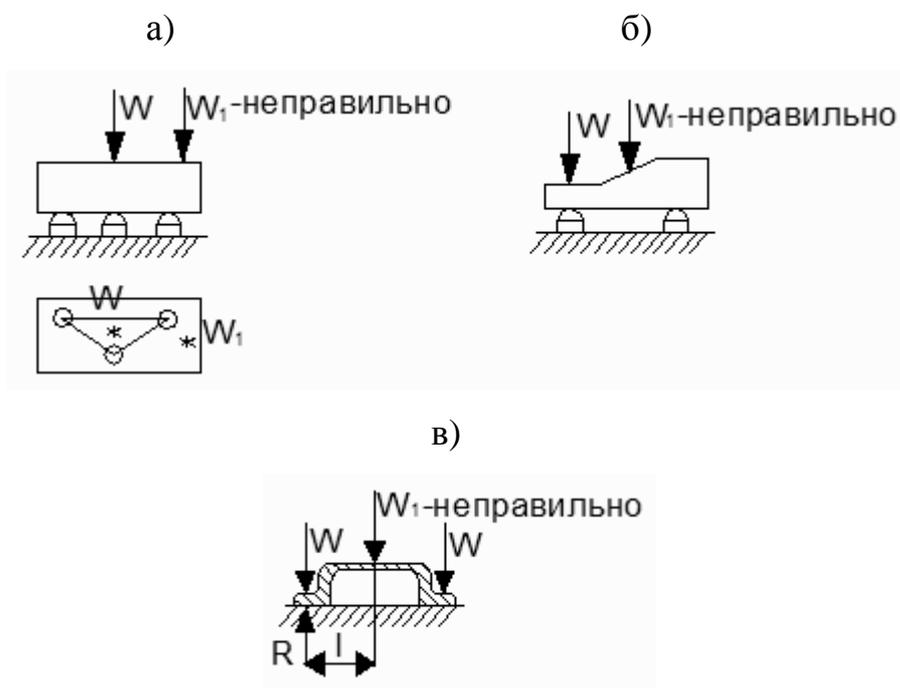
Схемы расположения сил зажима на заготовке.
